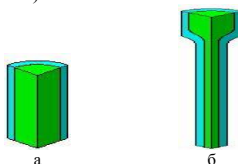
Заготовка із поздовжньою шаруватістю, отримана видавлюванням: а – вихідна заготовка; б - деталь
